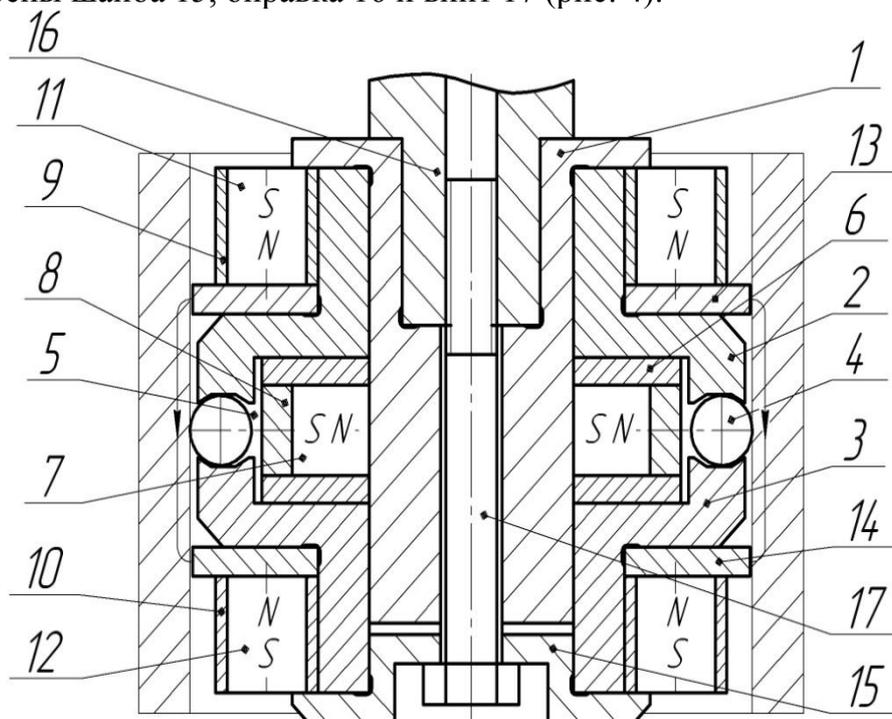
Конструкция раскатника для комбинированной магнитно-динамической отделочно-упрочняющей обработки поверхности отверстий
